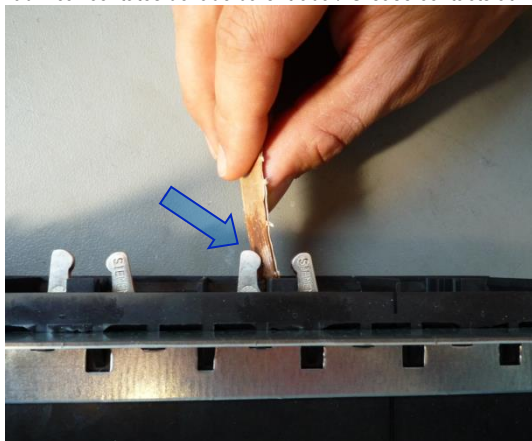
Deslocar para fora os contatos de ruptura / Pictures step 1 - main contacts drive out
